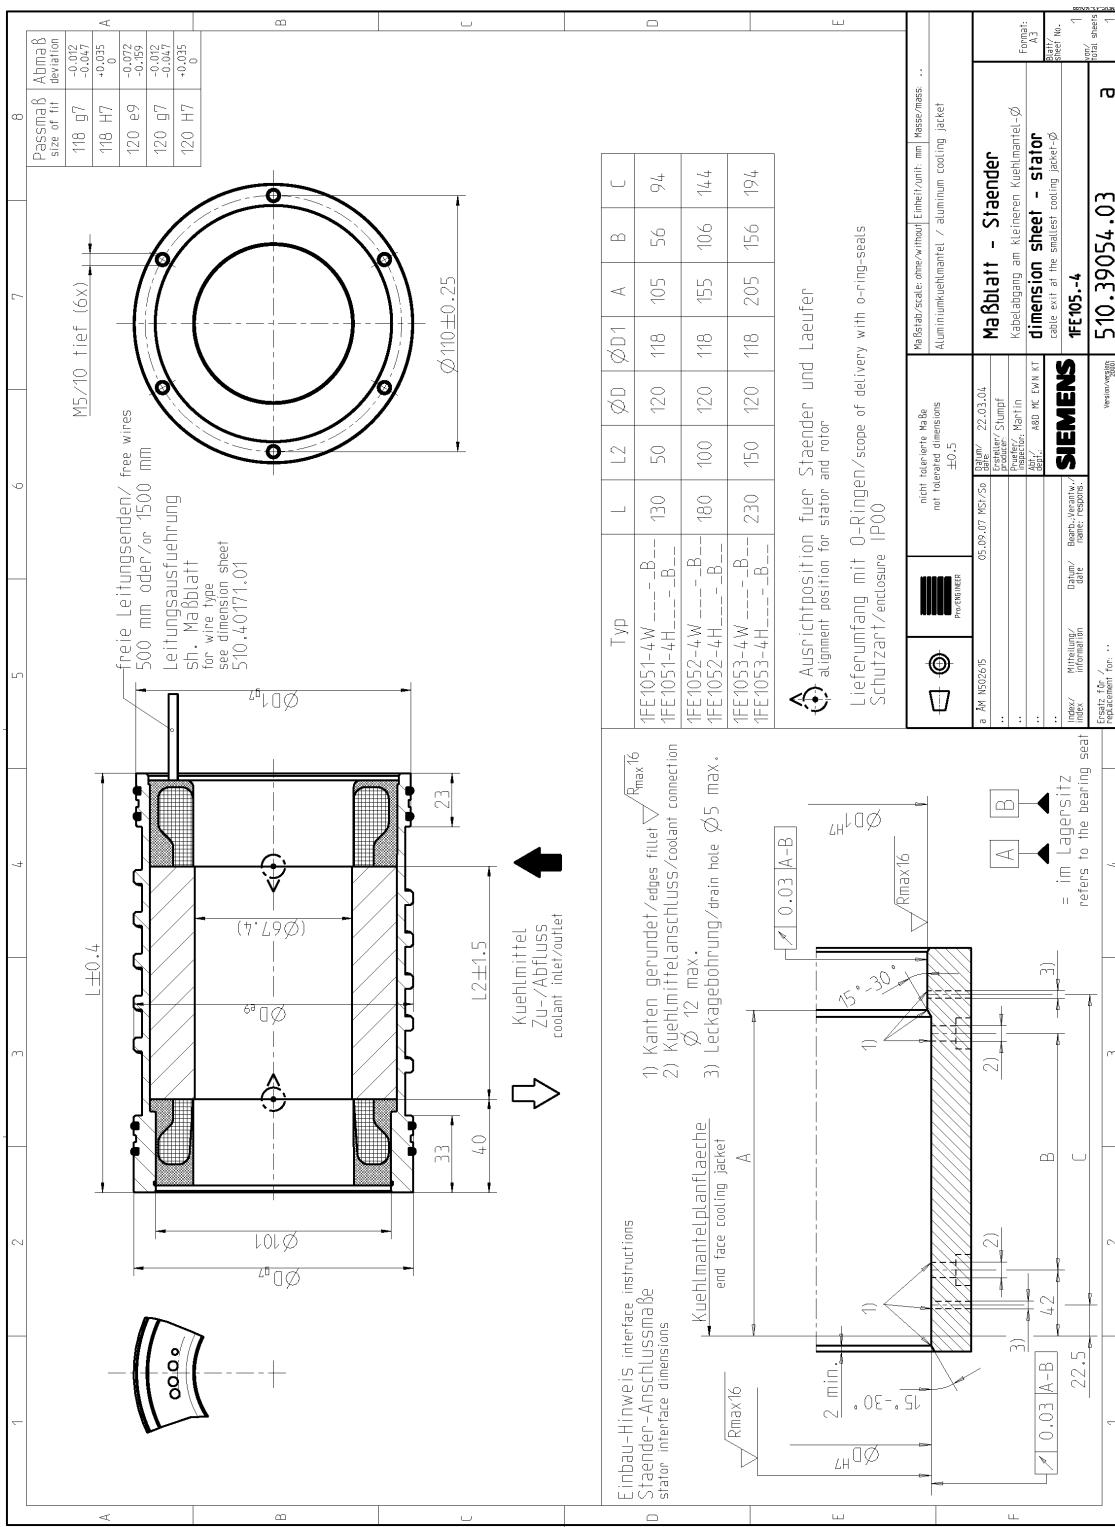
1FE105□-4, Ständer mit Kühlmantel, Kabelabgang am kleineren Kühlmanteldurchmesser
